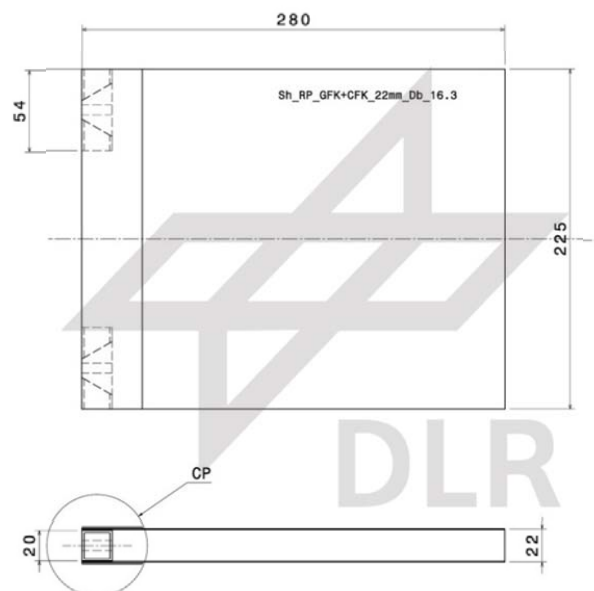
Sandwichprobekörper mit Randlasteinleitung zur Prüfung von Randlasteinleitungskonzepten im Sandwichtyp 618 HC unter flächenparalleler Schubbelastung.
